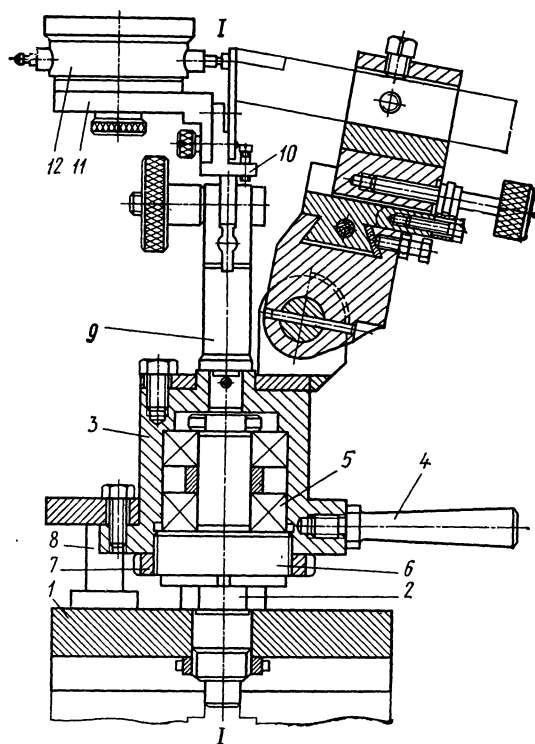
Приспособление для заточки и доводки резцов по задним поверхностям и радиусу при вершине
